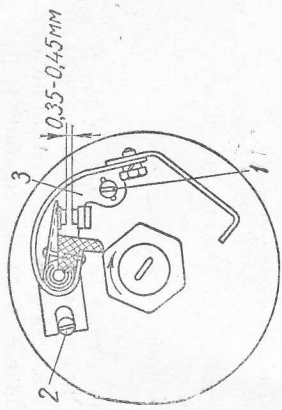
Схема расположения регулировочных винтов прерывателя: 1 — винт пластины неподвижного контакта; 2 — эксцентричный винт; 3 — планка.
